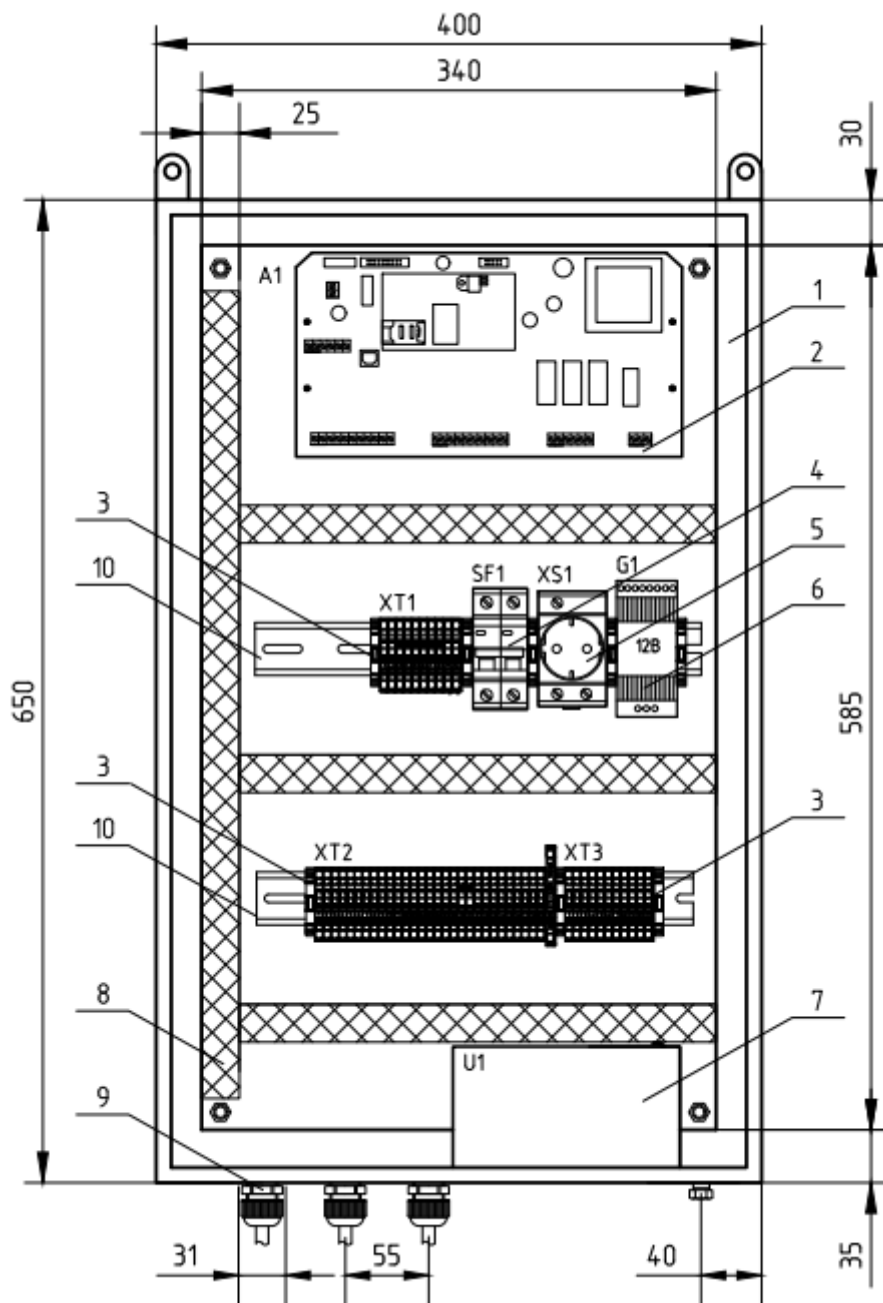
Общий вид (внутренний) и габаритные размеры шкафа ШСКД-1-У1.
